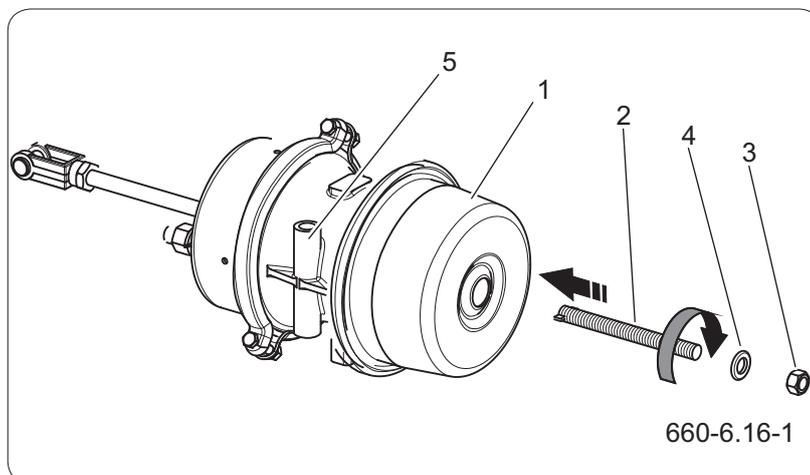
Аварийный выпуск тормозного цилиндра
